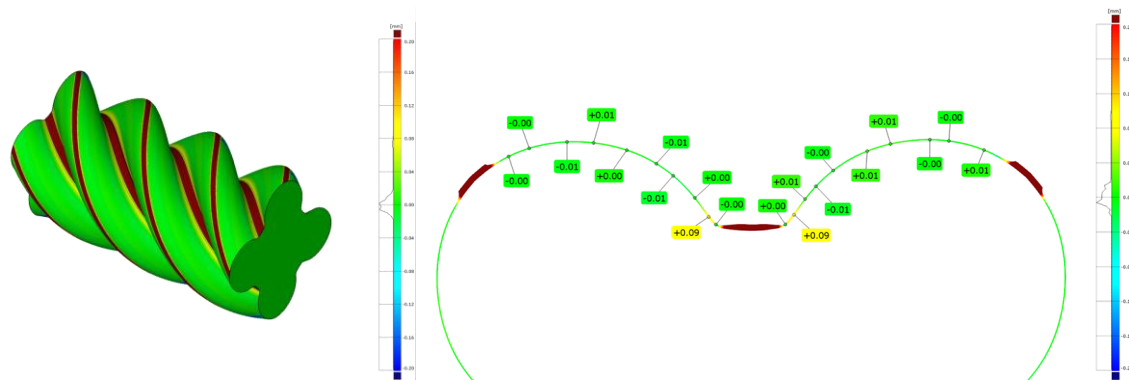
Desviación dimensional del compresor de tornillo sin fin macho simétrico.
